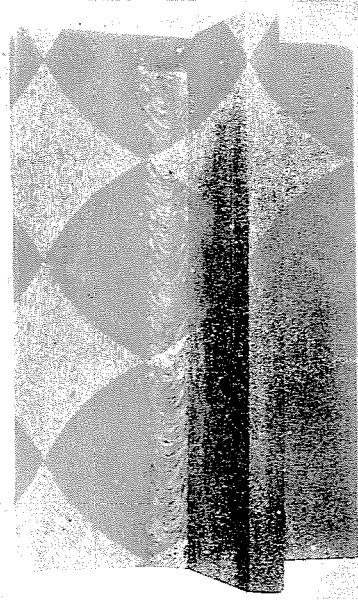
Kehlnaht ( $a = 7$  mm), von oben nach unten geschweißt
